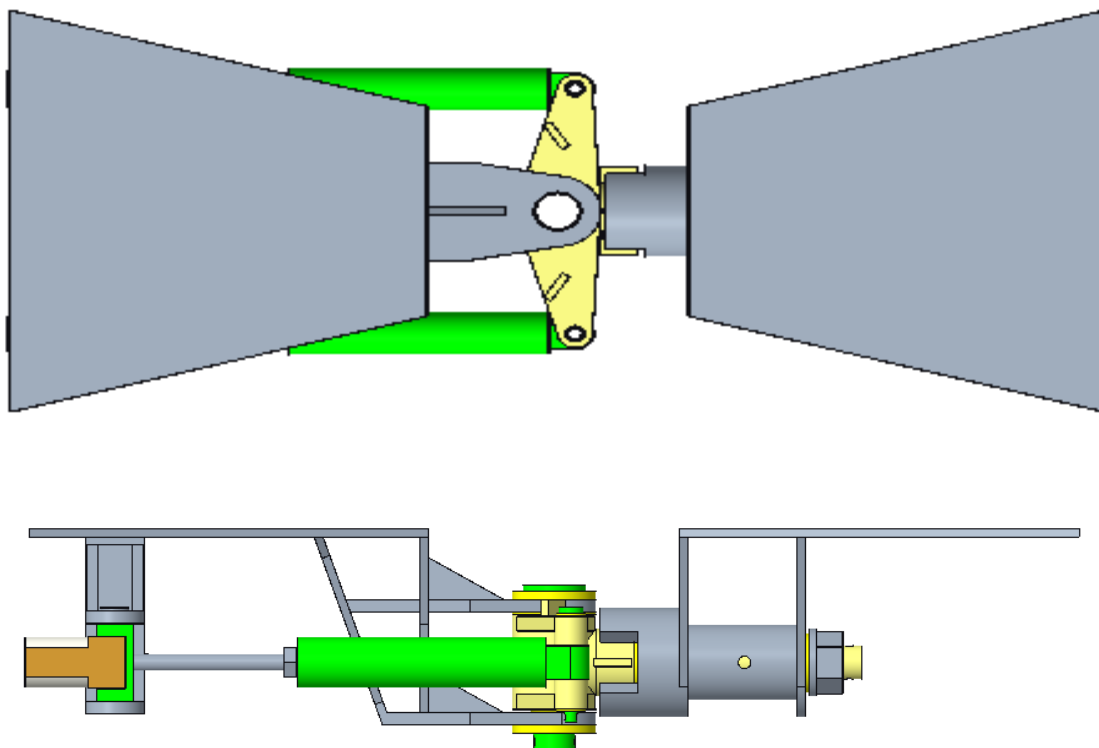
Vista en planta i alçat del conjunt de la direcció.
